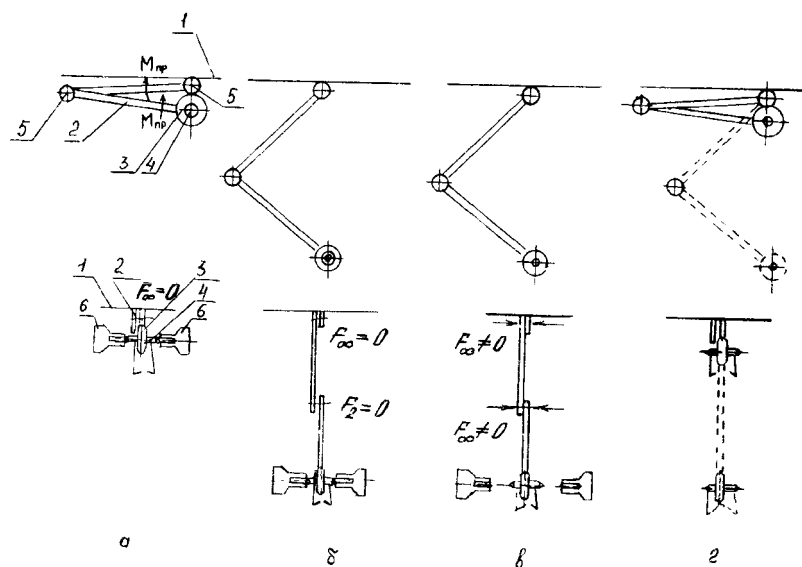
Схема переналадки сборочного приспособления:
